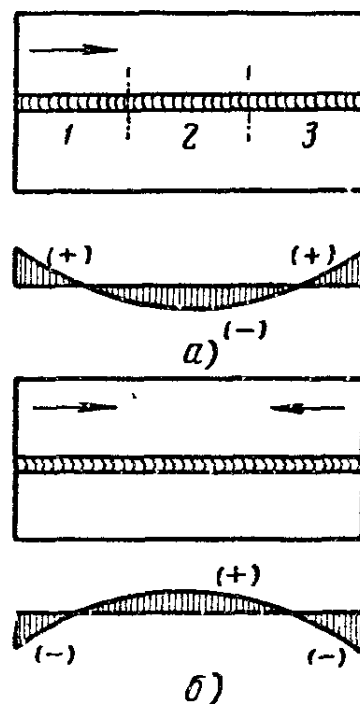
Напряжения от поперечной усадки в продольном сечении шва:
